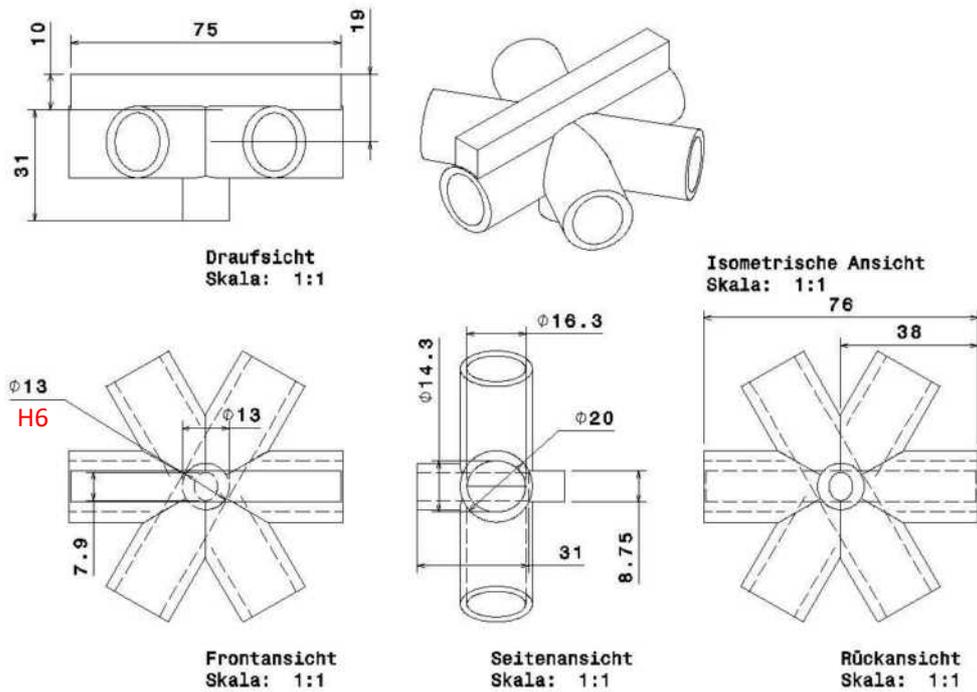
Element 10 (2D-Zeichnung) mit Toleranz
